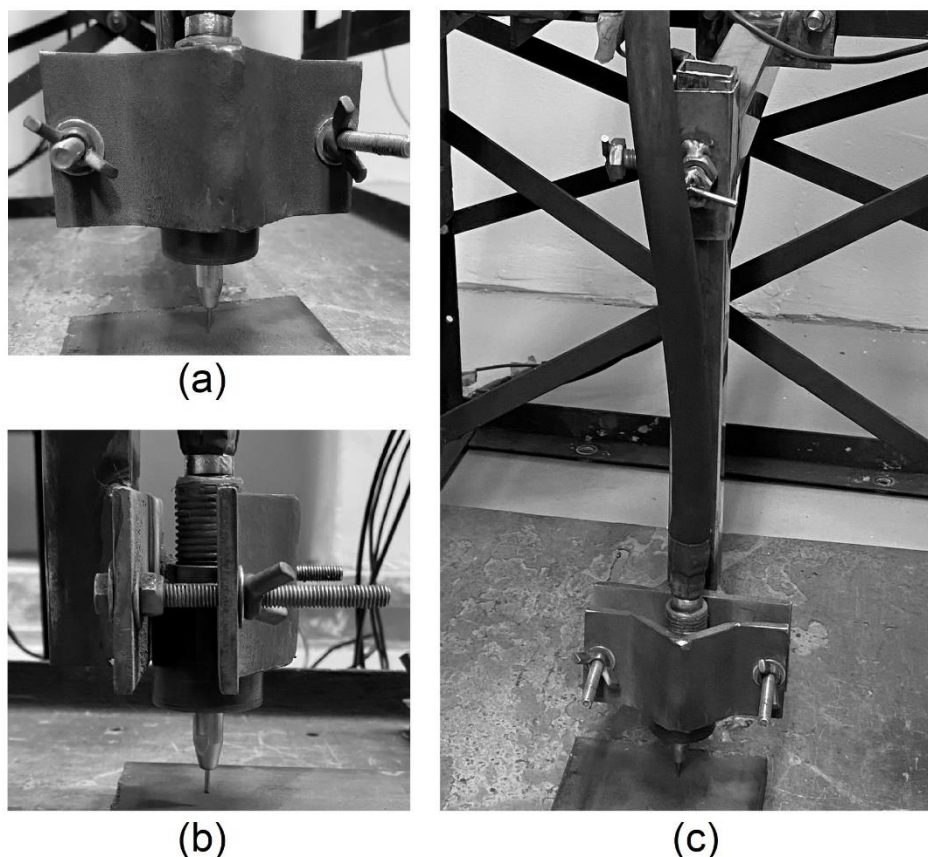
Sistema de fixação da tocha de soldagem. (a) Vista frontal, (b) vista lateral esquerda, (c) alavanca completa.
